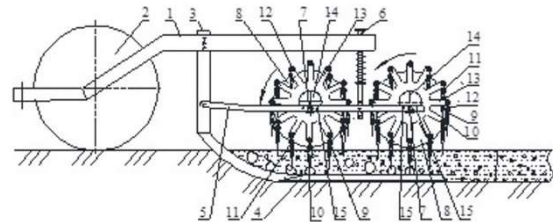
Схема культиватора для поверхневого обробітку ґрунту з голчатими робочими органами: 1 – рама; 2 – колеса; 3 – стійка; 4 – лапа; 5 – полоз; 6 – пристрій; 7 – вісь; 8 – диски; 9 – голки; 10 – вістря голок; 11 – вал; 12 – кривошип; 13 – хрестовина; 14 – ексцентриковий механізм; 15 – пристрій регулювальний
